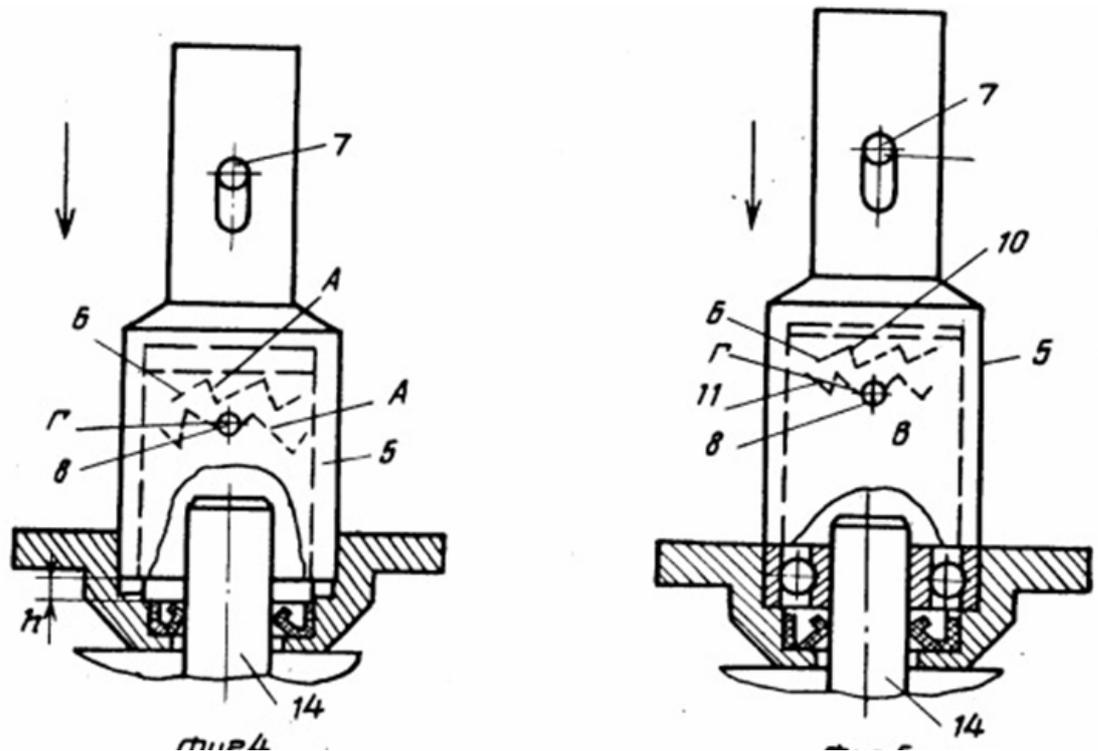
Рабочая головка в момент запрессовки в корпус манжеты и в момент запрессовки подшипника (А.С. SU1344567)
